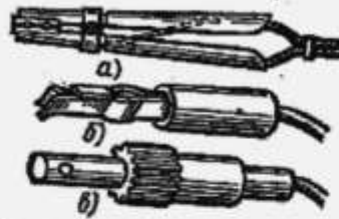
Электрододержатели для ручной дуговой сварки:
